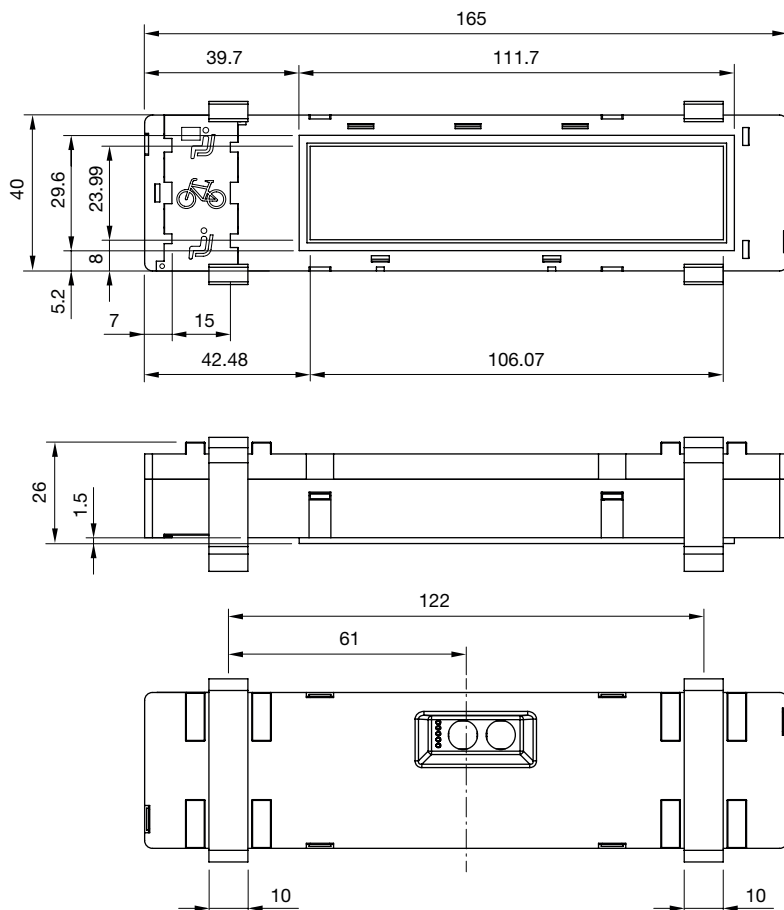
Abmessungen (mm) Gehäuse Clip-Befestigung.
